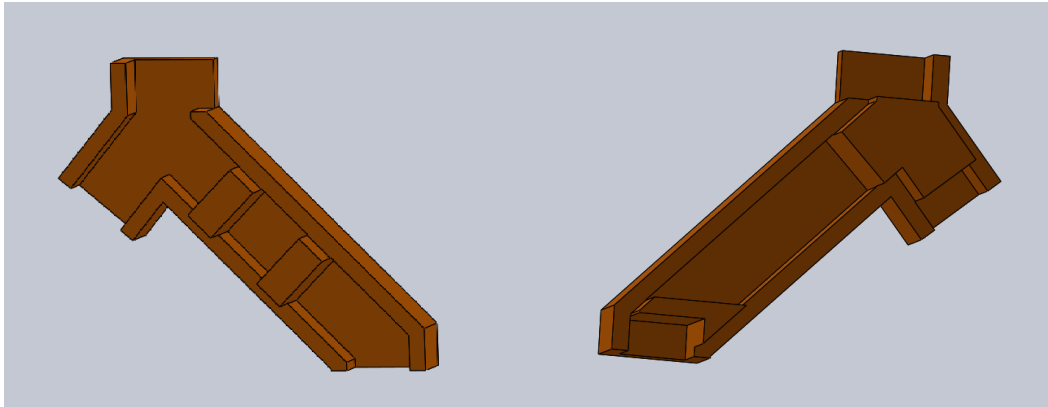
A la izquierda: Pieza M22.1. A la derecha: Pieza M22.2.
